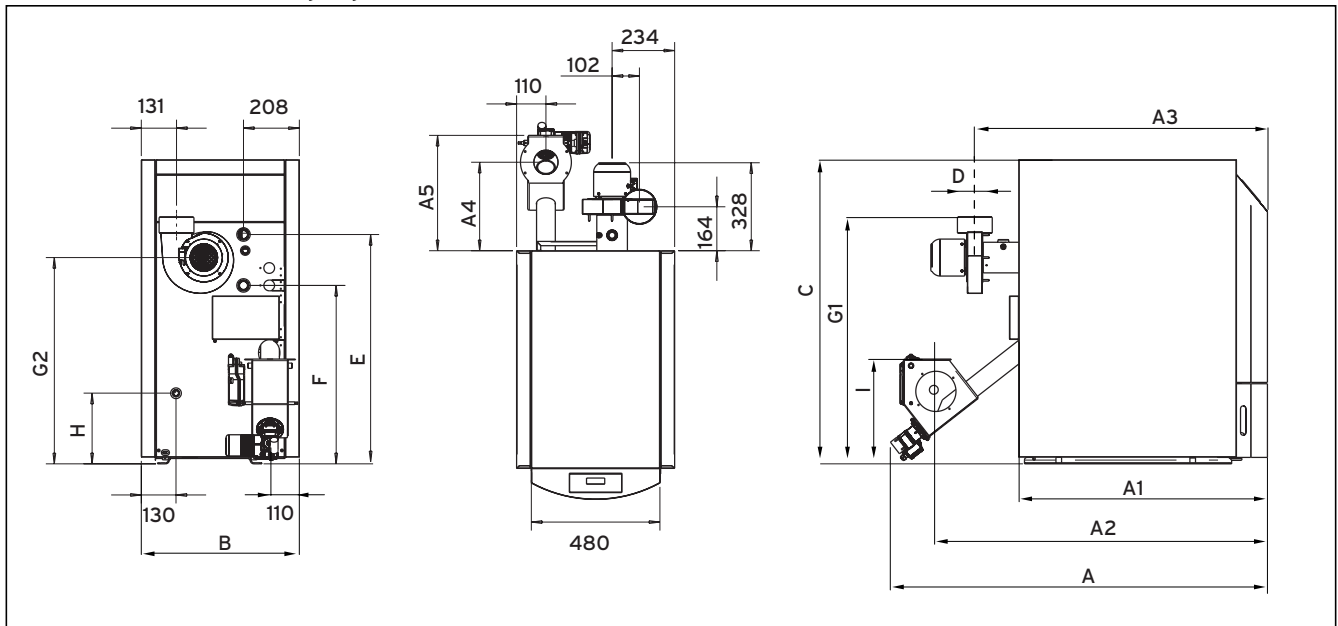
Abmessungen: Pelletkessel mit Schneckenaustragung
